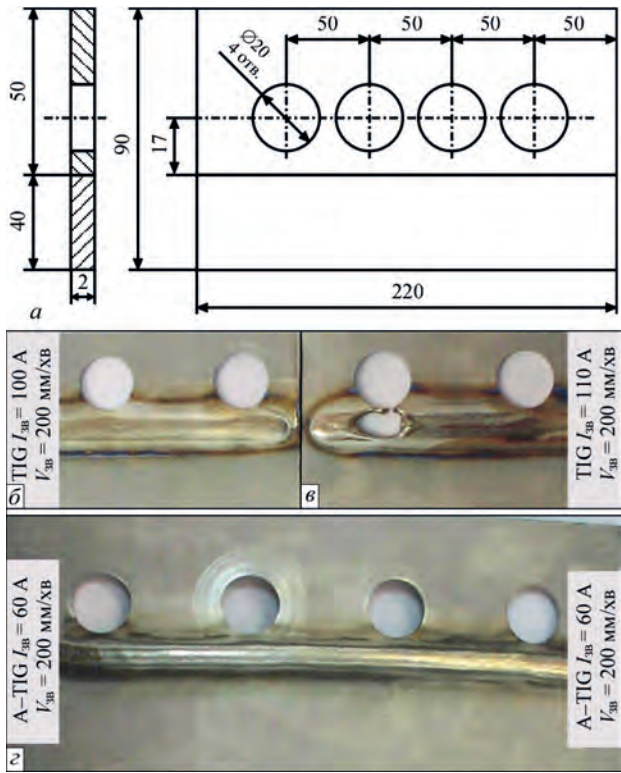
Зовнішній вигляд фрагментів зварних зразків-імітаторів зі сплаву ВТ-20 завтовшки δ = 2 мм при повному проплавленні: схема підготовки зразка-імітатора (а); TIG зварювання, струм зварювання – 100 А (б) та 110 А (в); A-TIG зварювання, струм зварювання – 60 А (г)
